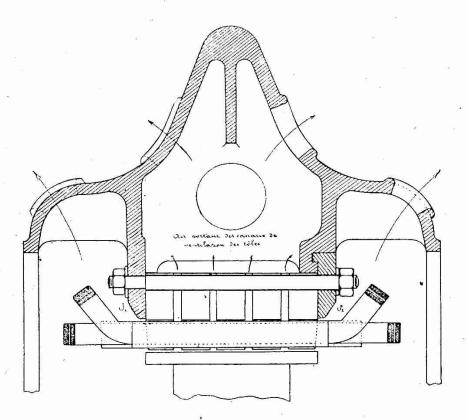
Coupe d'une carcasse avec une joue de serrage indépendante Enroulement à deux étages de bobines
